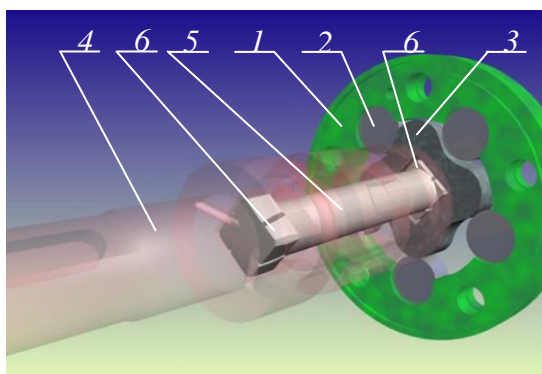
Компенсирование планетарного движения вытеснителей с помощью карданной передачи: 1 – охватывающий вытеснитель; 2 – ролики; 3 – охватываемый вытеснитель; 4 – вал гидромотора; 5 – кардан; 6 – муфты карданной передачи
